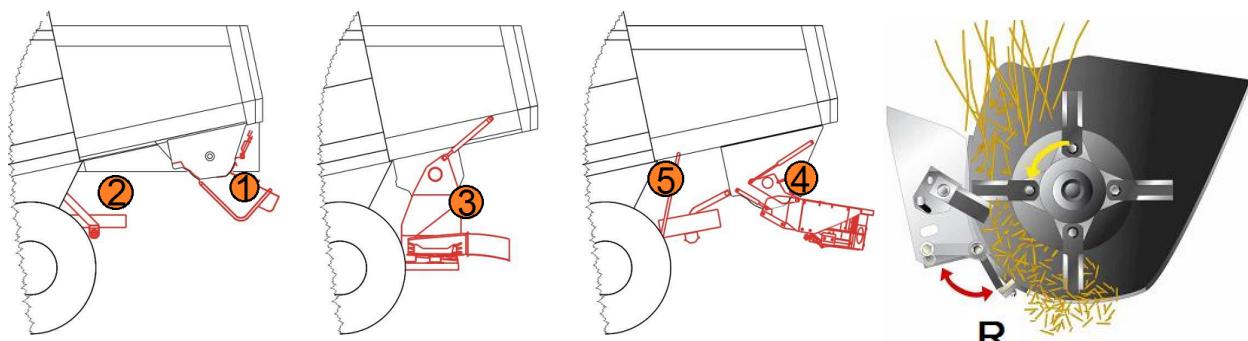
Соломоизмельчитель и половоразбрасыватель
